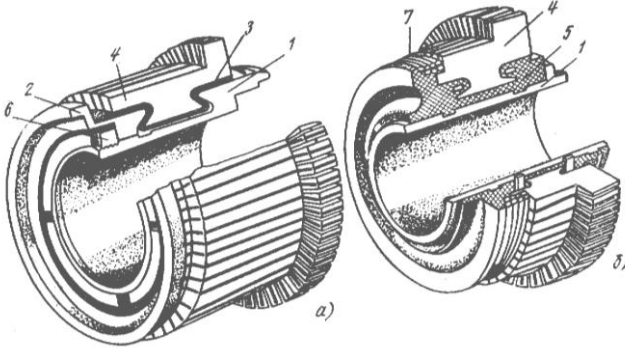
Колектор машини постійного струму з металевим (а) і пластмасовим (б) корпусами: 1 – корпус; 2 – натискний фланець; 3 – ізоляційні манжети; 4 – колекторні пластини; 5 – пластмаса; 6 – запірне кільце; 7 – бандаж
